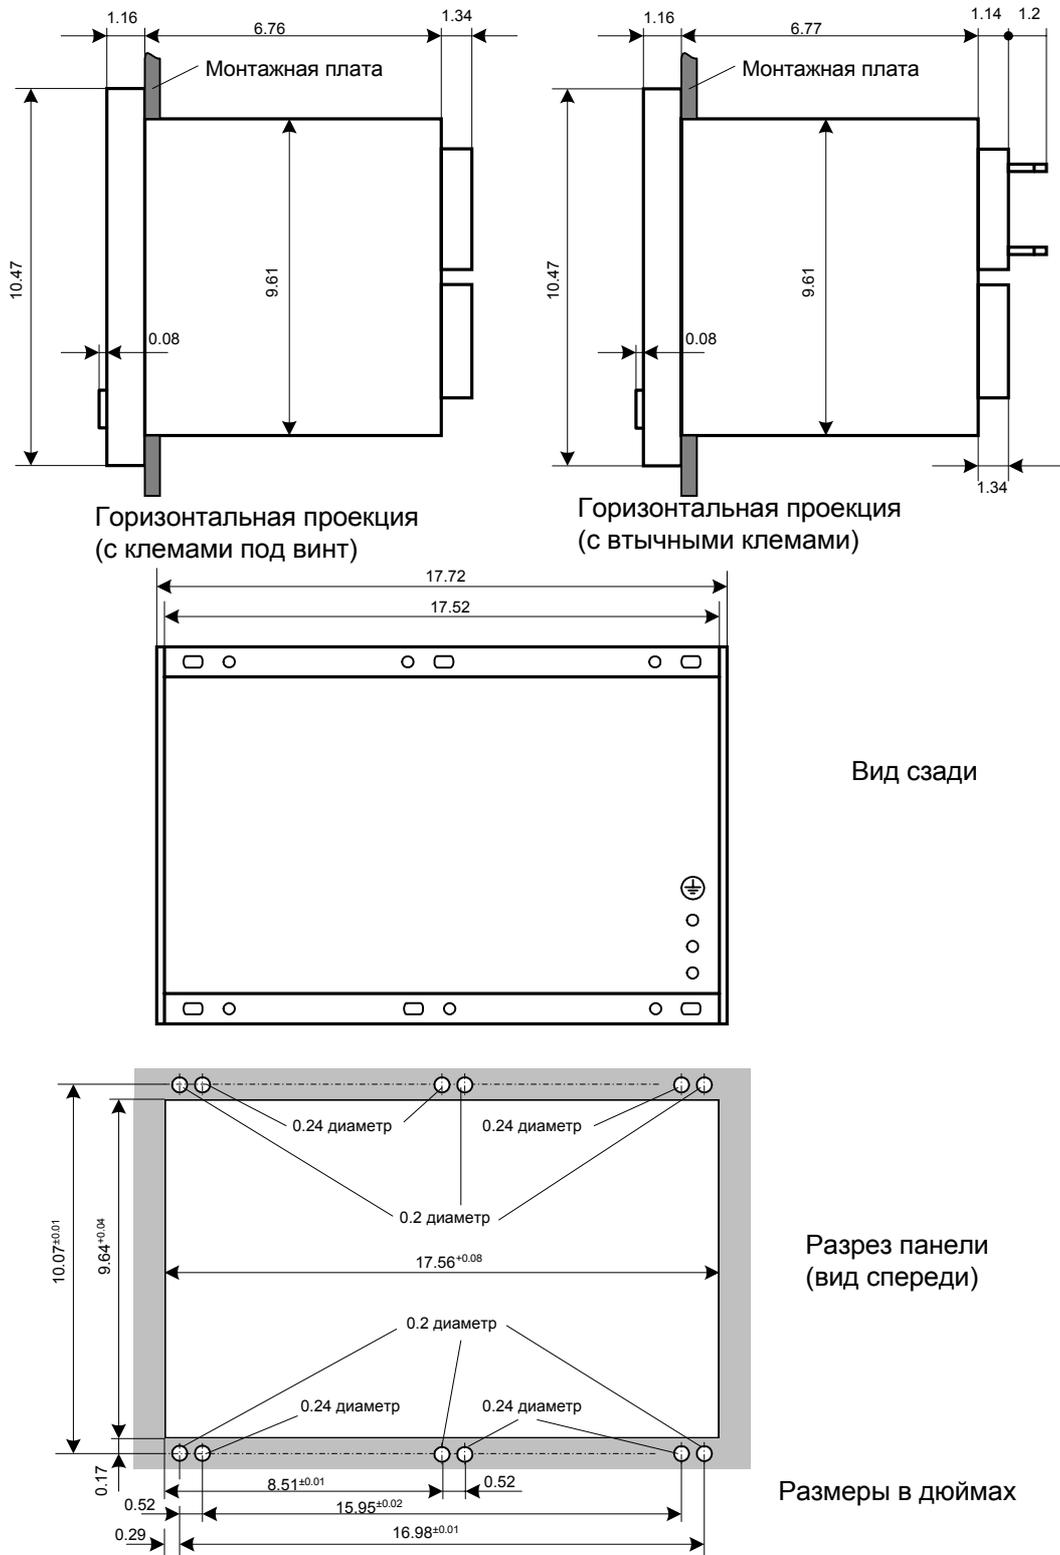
Размеры устройства 7SJ63 для встраивания в панель или в шкаф (размер корпуса $1/1$)
